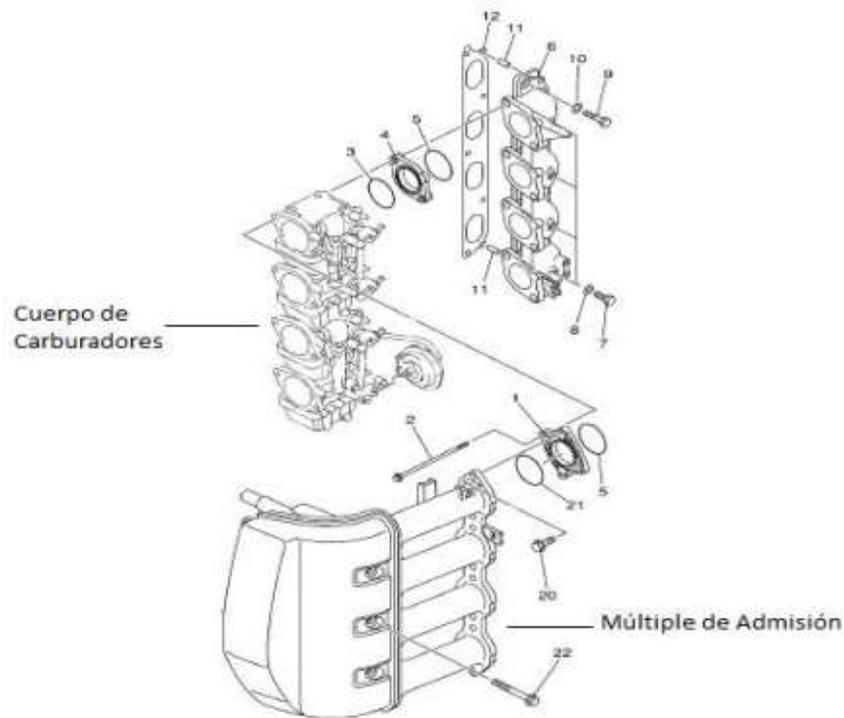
Sistema de combustible de cuerpo de carburadores de un motor F75 Hp
